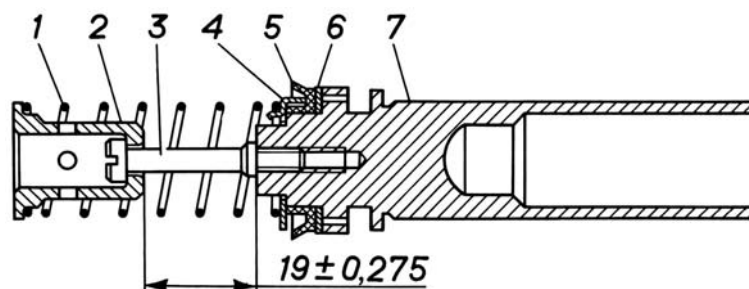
Первичный поршень главного цилиндра: 1 - пружина; 2 - держатель пружины; 3 - винт; 4 - упорная шайба; 5 - манжета; 6 - шайба; 7 - поршень
